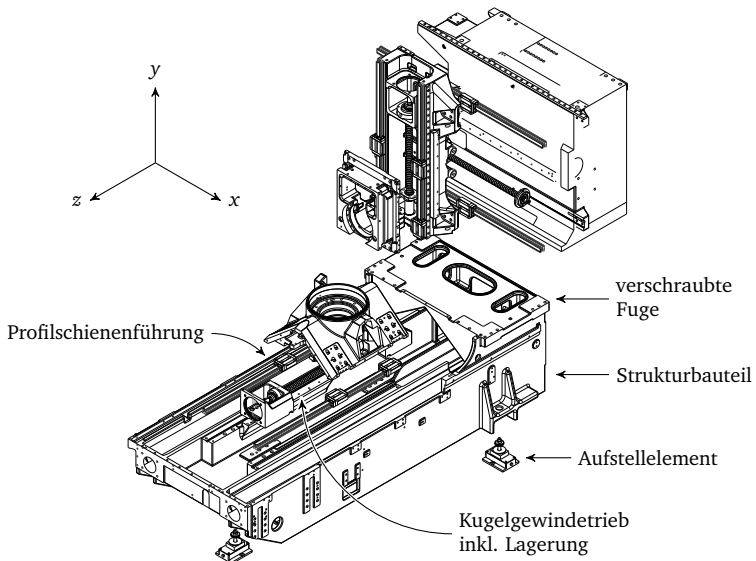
Typische Komponenten der Maschinenstruktur einer spanenden Werkzeugmaschine mit zugehörigem Maschinenkoordinatensystem
